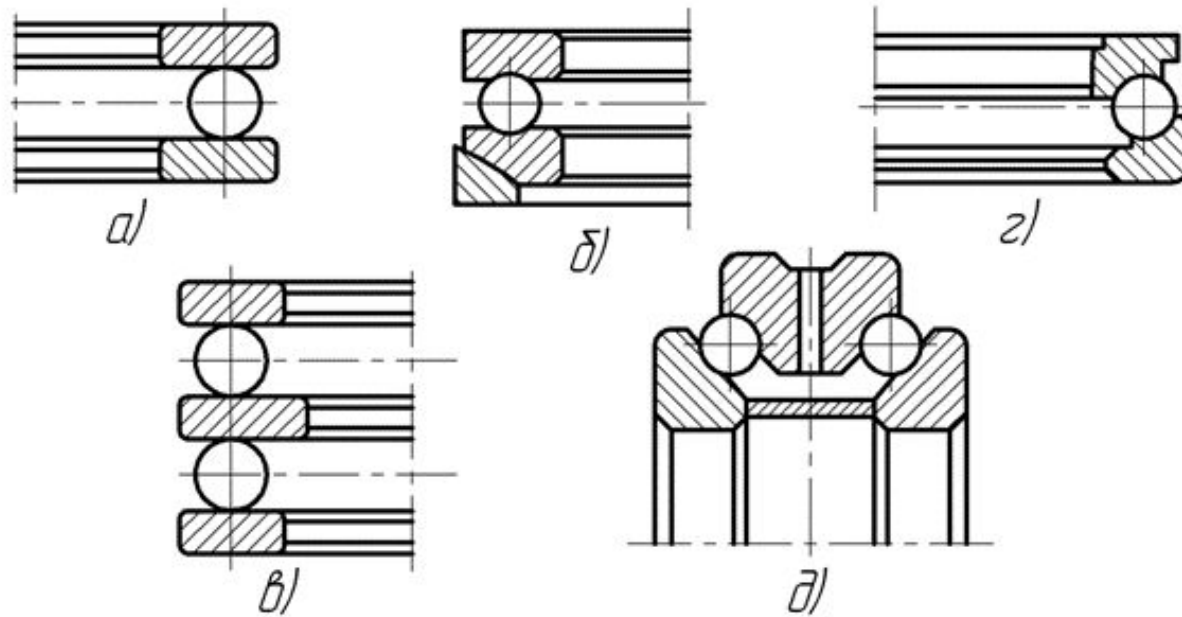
Подшипники упорные и упорно-радиальные шариковые исполнений:
